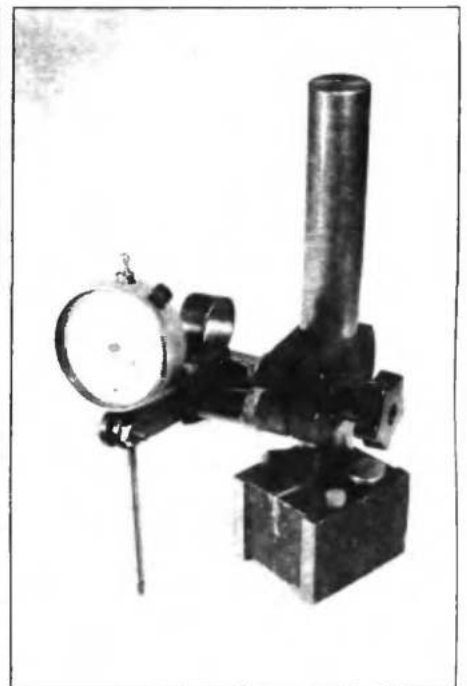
Магнитная стойка с индикатором часового типа для измерения биения валов
